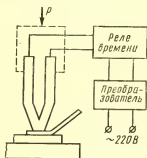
Схема сварки давлением с косвенным импульсным нагревом
